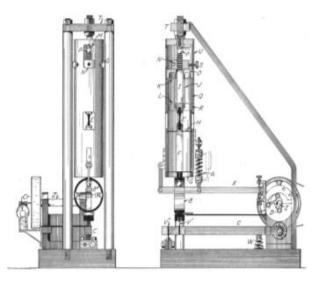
Máquina para ensayo de fatiga de esfuerzo axial.
